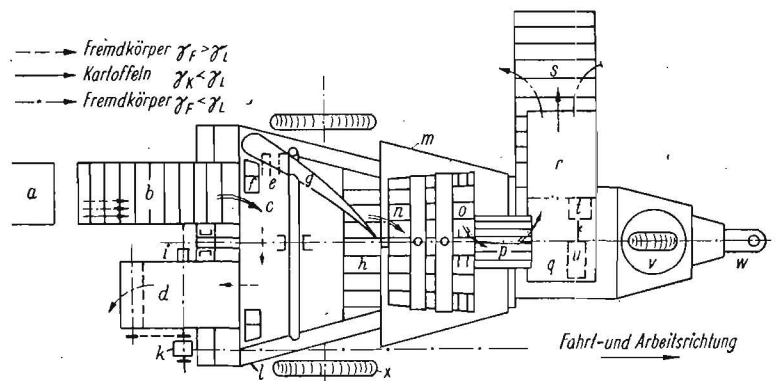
Grundrißschema der Trennanlage II (Funktionselemente)
